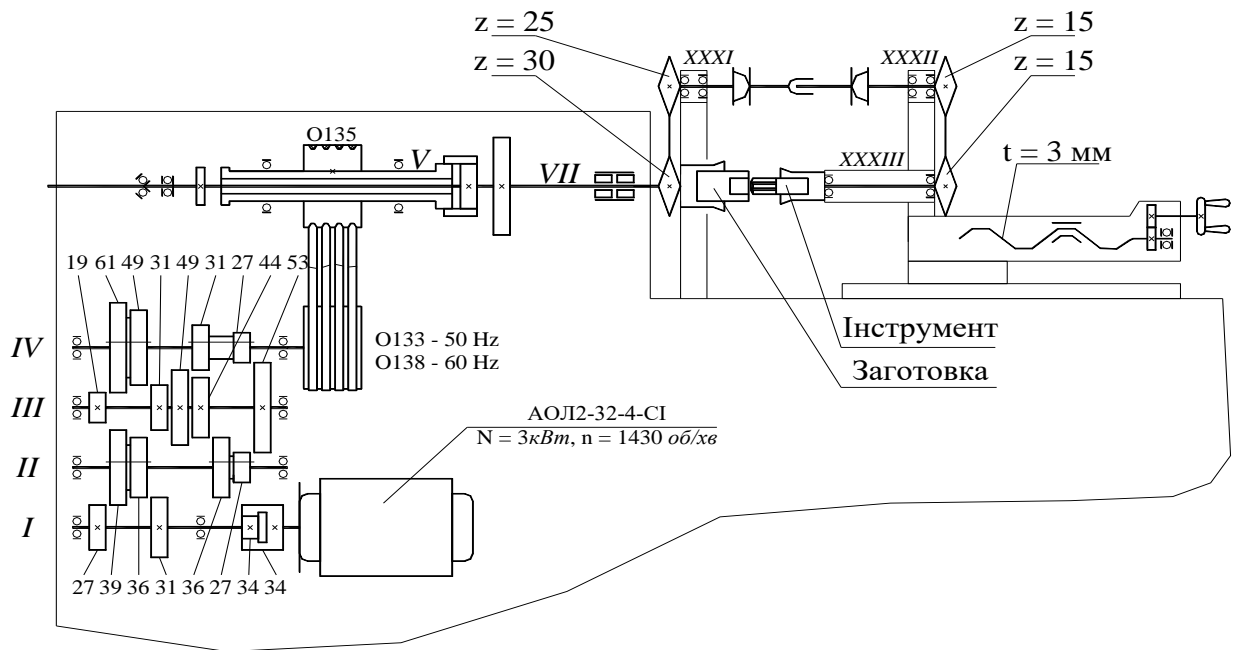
Фрагмент кінематичної схеми модернізованого верстата
